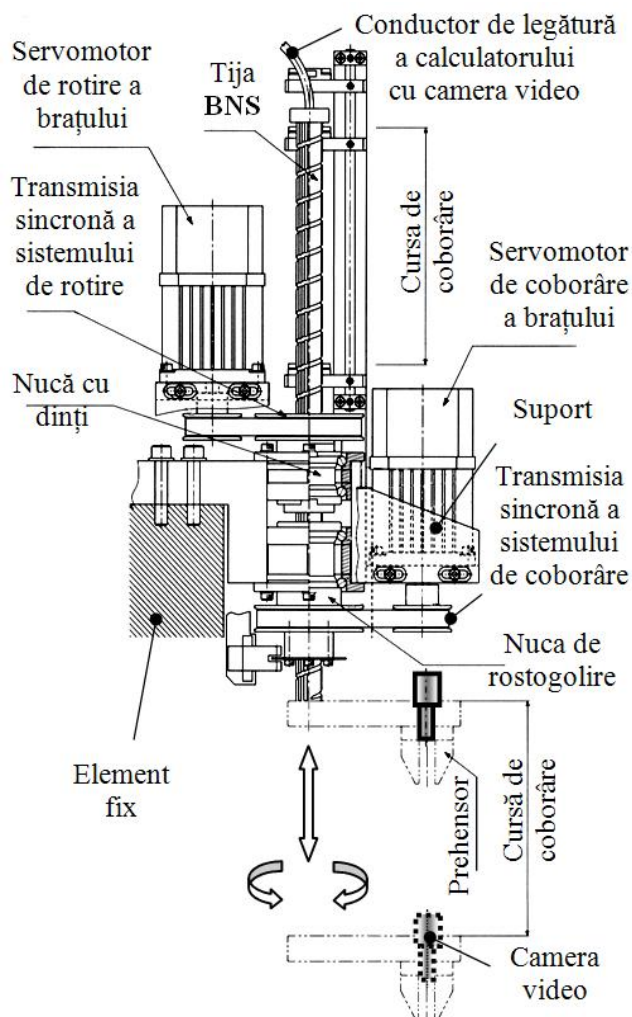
pt varianta 7, varianta 8 si varianta 9
